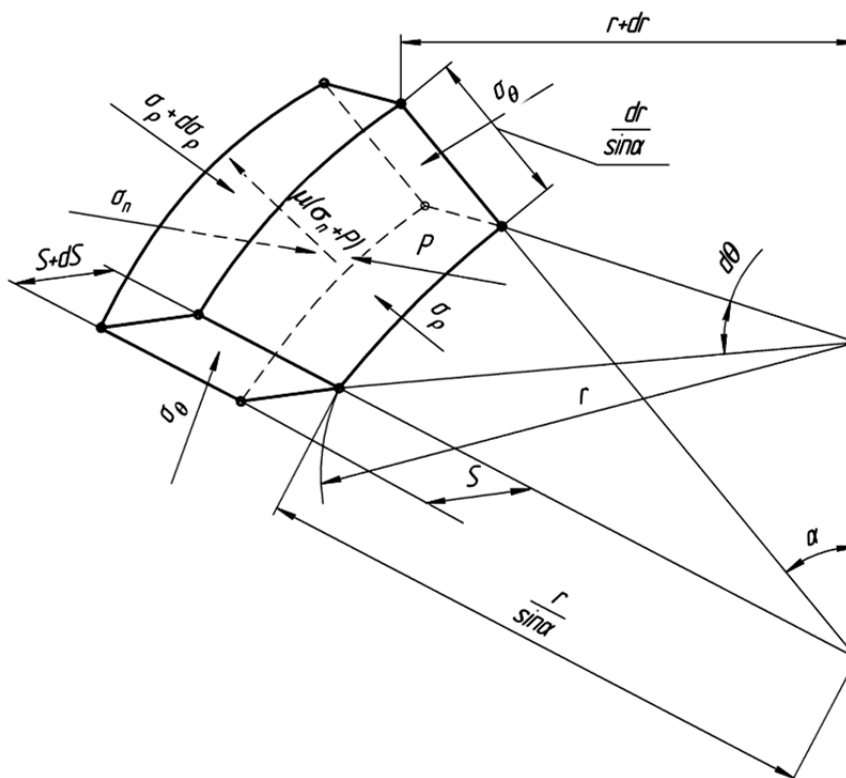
Елементарний об'єм в стінці zdeформованої заготовки
